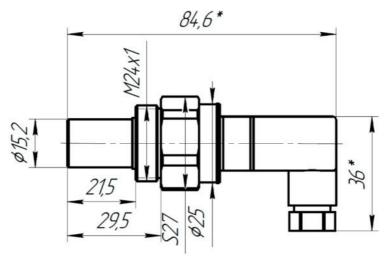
Установочные и габаритные размеры преобразователя ДВ2ТСМ-1Т-1П-В.
